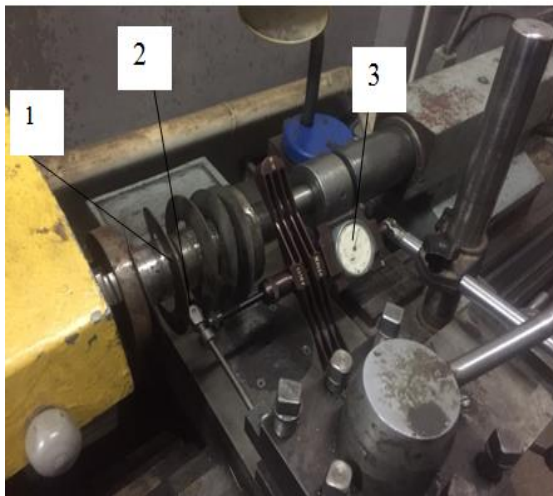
Загальний вигляд експериментальної установки для калібрування кроку витків гвинтових заготовок: 1 – гвинтова заготовка; 2- клин для здійснення калібрування гвинтової заготовки; 3- динамометр
